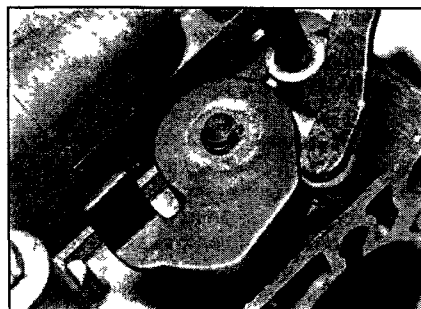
,б. Установка крышки системы вентиляции картера (кулачок ускорительного насоса)
